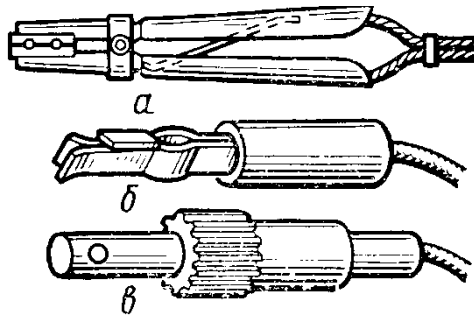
Електродотримачі для ручного дугового зварювання:
